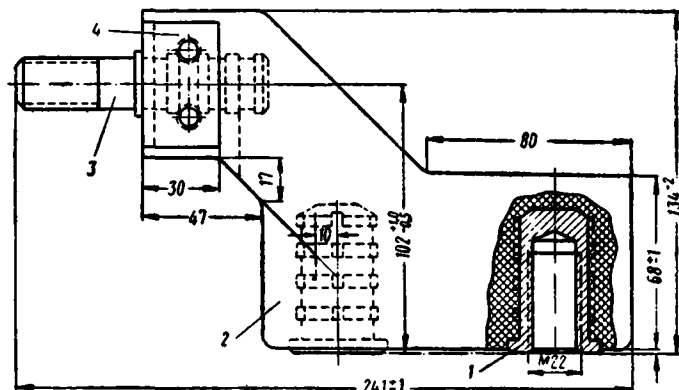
Кронштейн щеткодержателя тягового двигателя ДК-103Г, изготовленный на основе стеклопластика АГ-4В:
